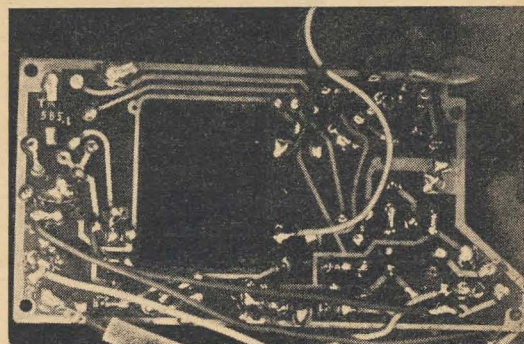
Ansicht des Chassis mit gedruckter Verdrahtung
